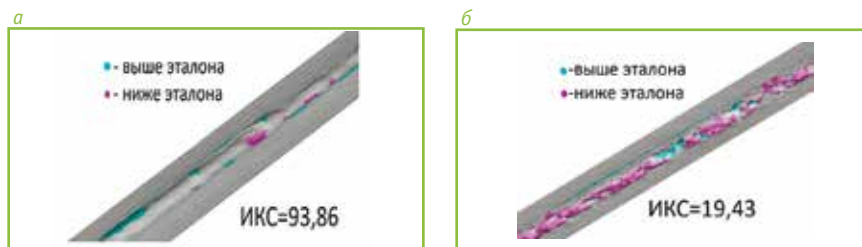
Цифровые реплики корневой поверхности сварного шва РД (111)
